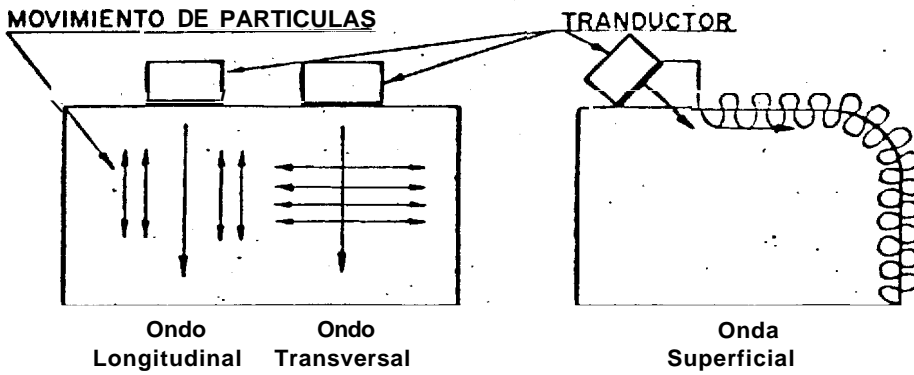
ONDAS LONGITUDINALES - TRANSVERSALES Y SUPERFICIALES (Ref. 13)
